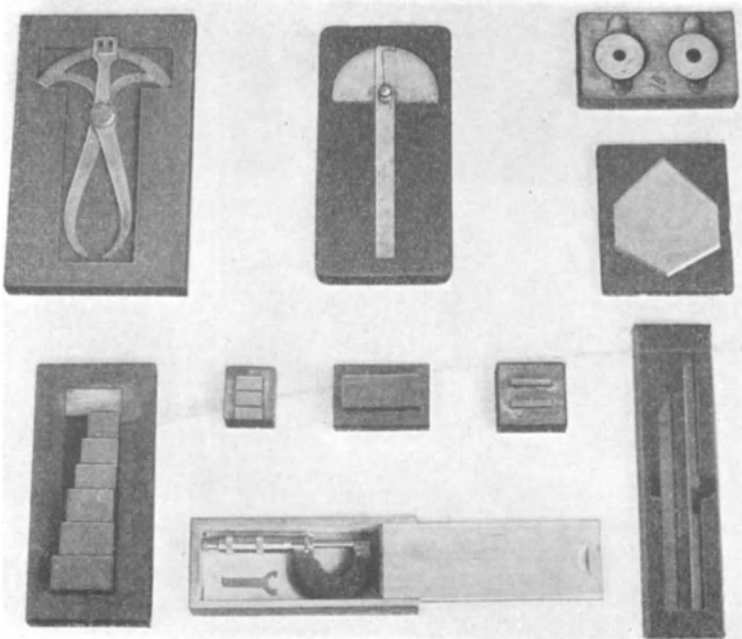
Meßwerkzeuge auf Holzbrettchen.
